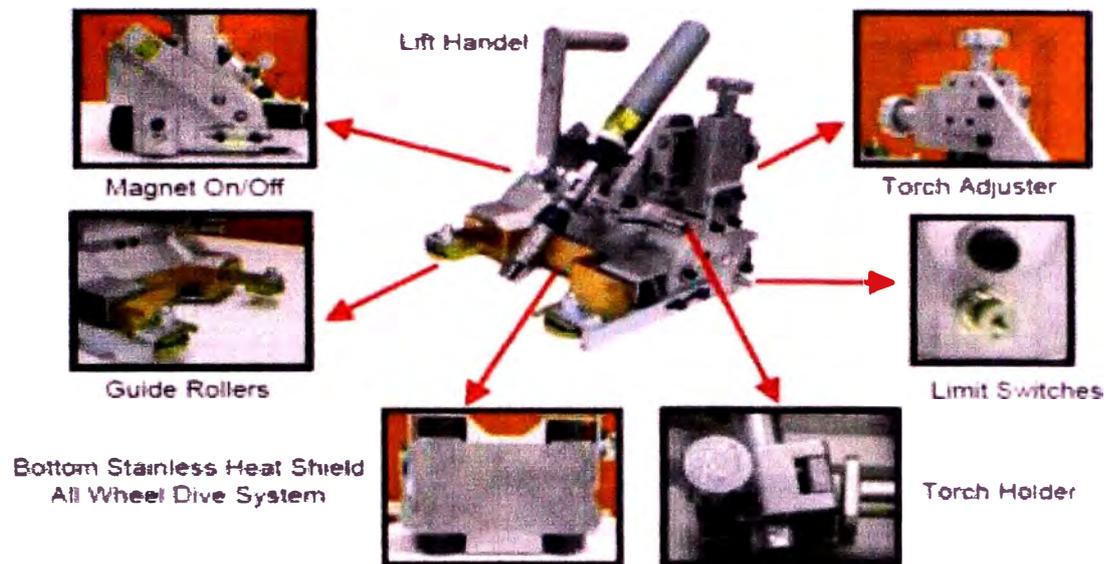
Equipo de Corte WELD-HANDY MULTI
